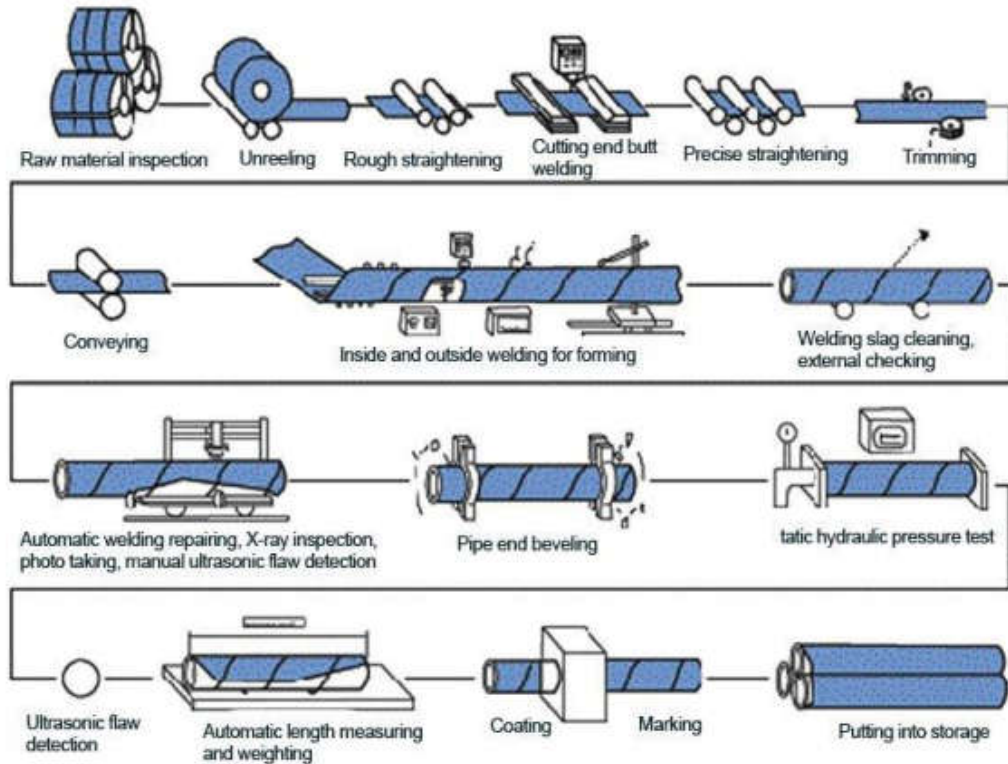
Technique de fabrication des tubes soudés en spirale [12]
